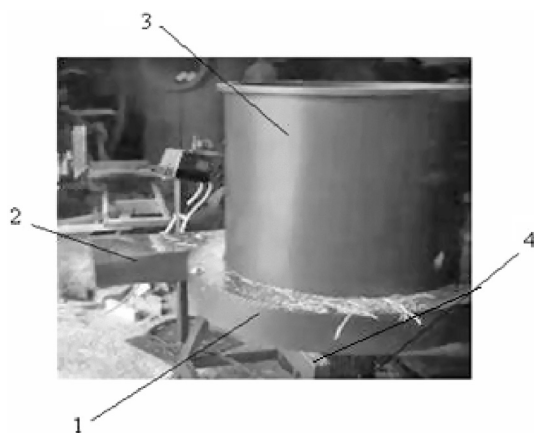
Усовершенствованный образец резчика рулонов — кормораздатчик ИРК-01.1:
